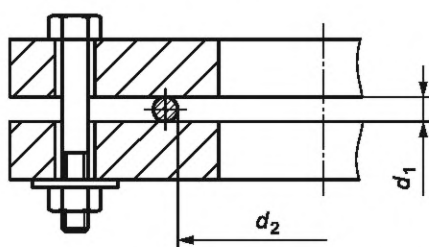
Фланцы, соединенные болтами с уплотнительным кольцом
